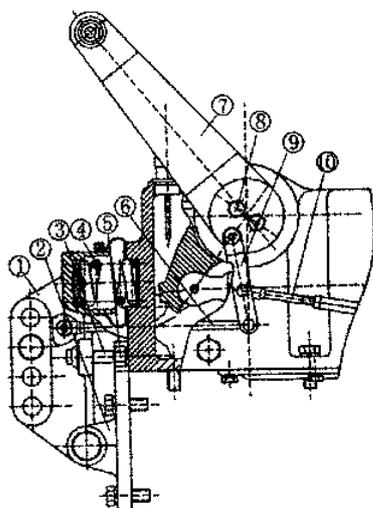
15. Регулирующий механизм комплексной регулировки силы и положения
